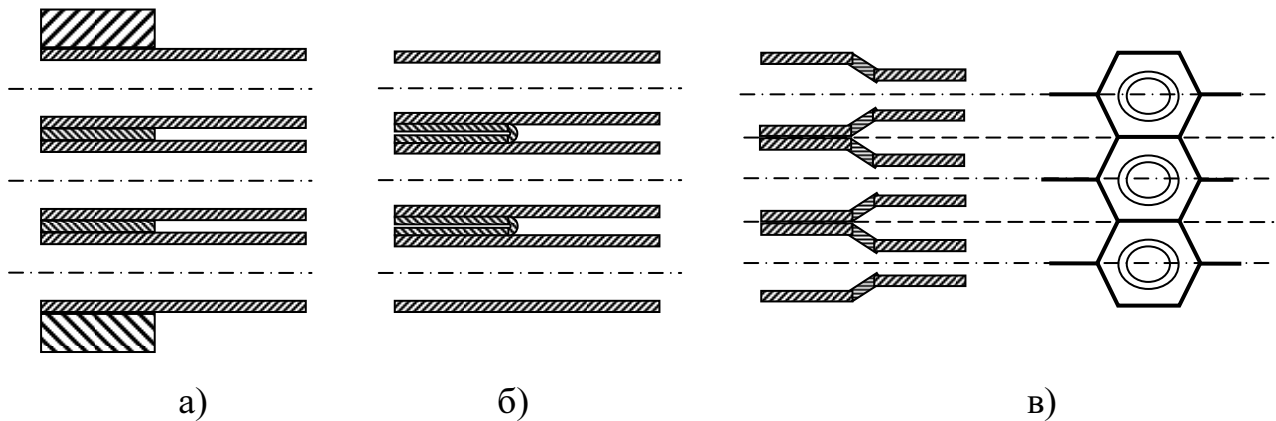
Изготовление пучковых теплообменных аппаратов: а) с толстостенными трубными досками — сварка-пайка высокопрочным припоем; б) с тонкостенными трубными досками (ТТД) — гидровзрывная штамповка ТТД и сварка-пайка; в) ТА без трубных досок (взрывная формовка раструбов и их сварка-пайка)
